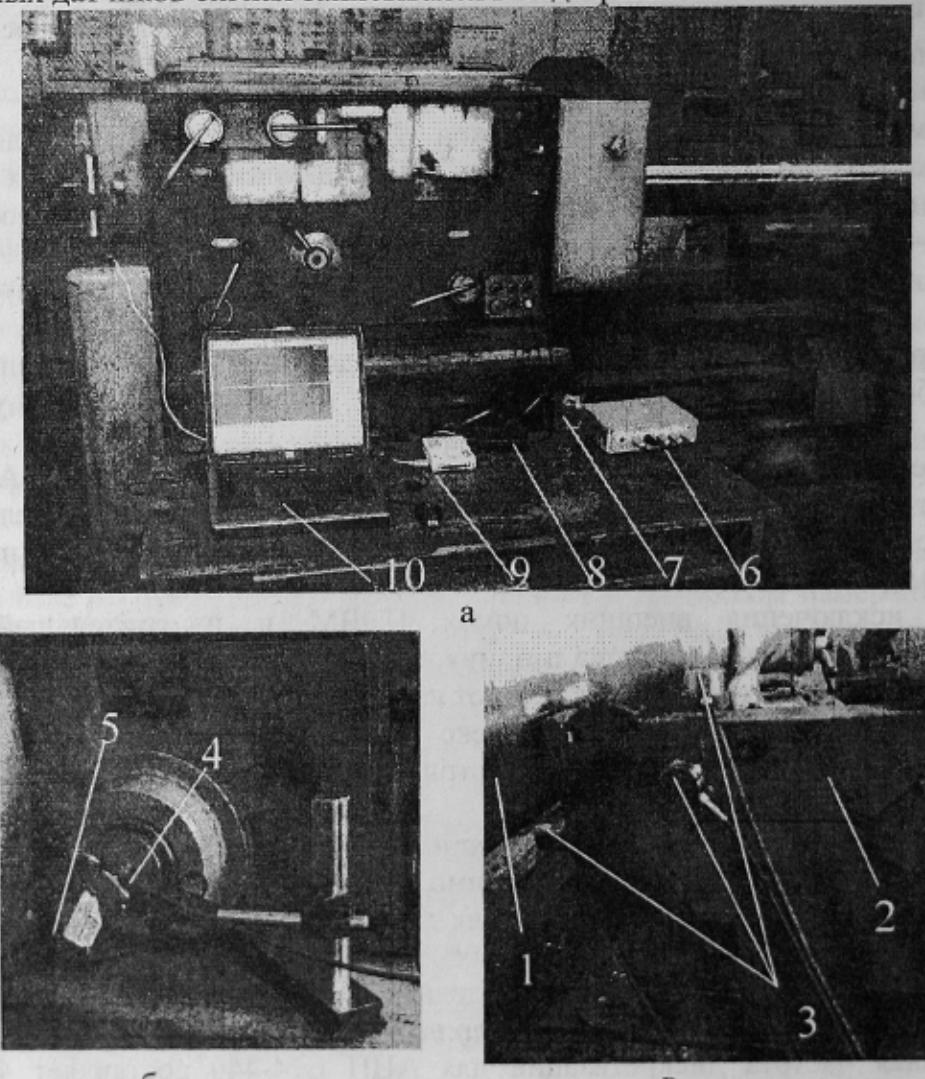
Вимірювальний стенд: а- загальний вигляд реєструючої апаратури; б- установка датчика обертання на шпинделі токарного станка мод. 1A64; в- установка датчиків вибрації на прорезному резці з ламельним суппортом.
